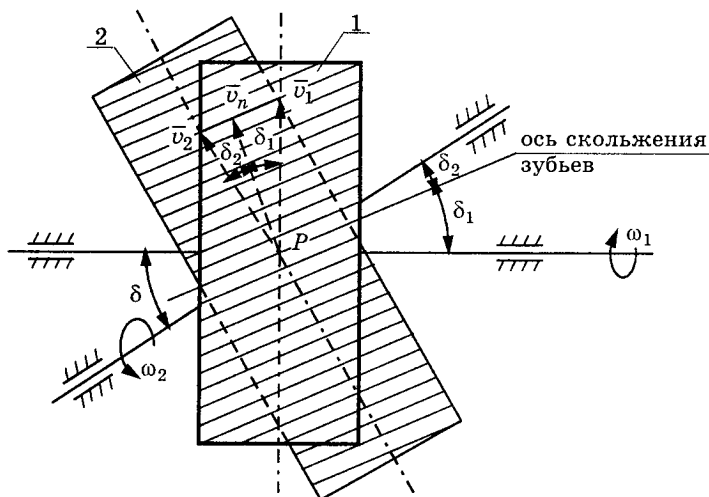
К определению передаточного отношения винтовой зубчатой передачи
